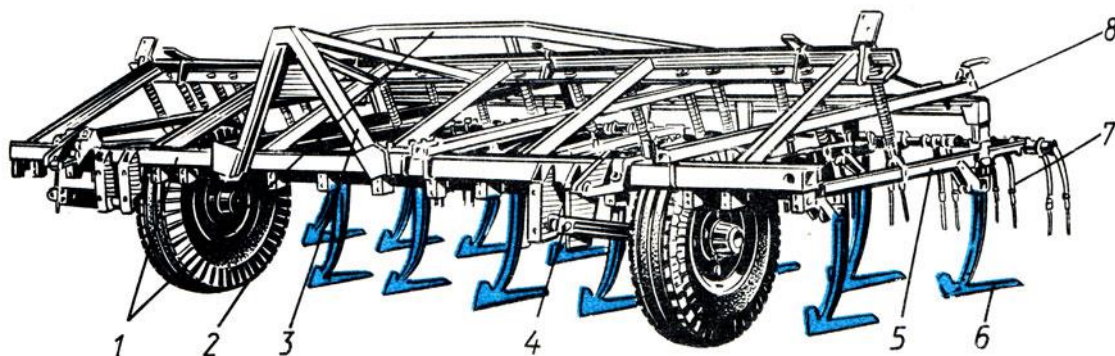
Навесной культиватор для сплошной обработки почвы: 1 - рама; 2 - колесо; 3 - замок автосцепки; 4 - механизм регулирования глубины; 5 - грядилы; 6 - стрельчатая лапа; 7 - пружинная борона; 8 - механизм для навески борон
